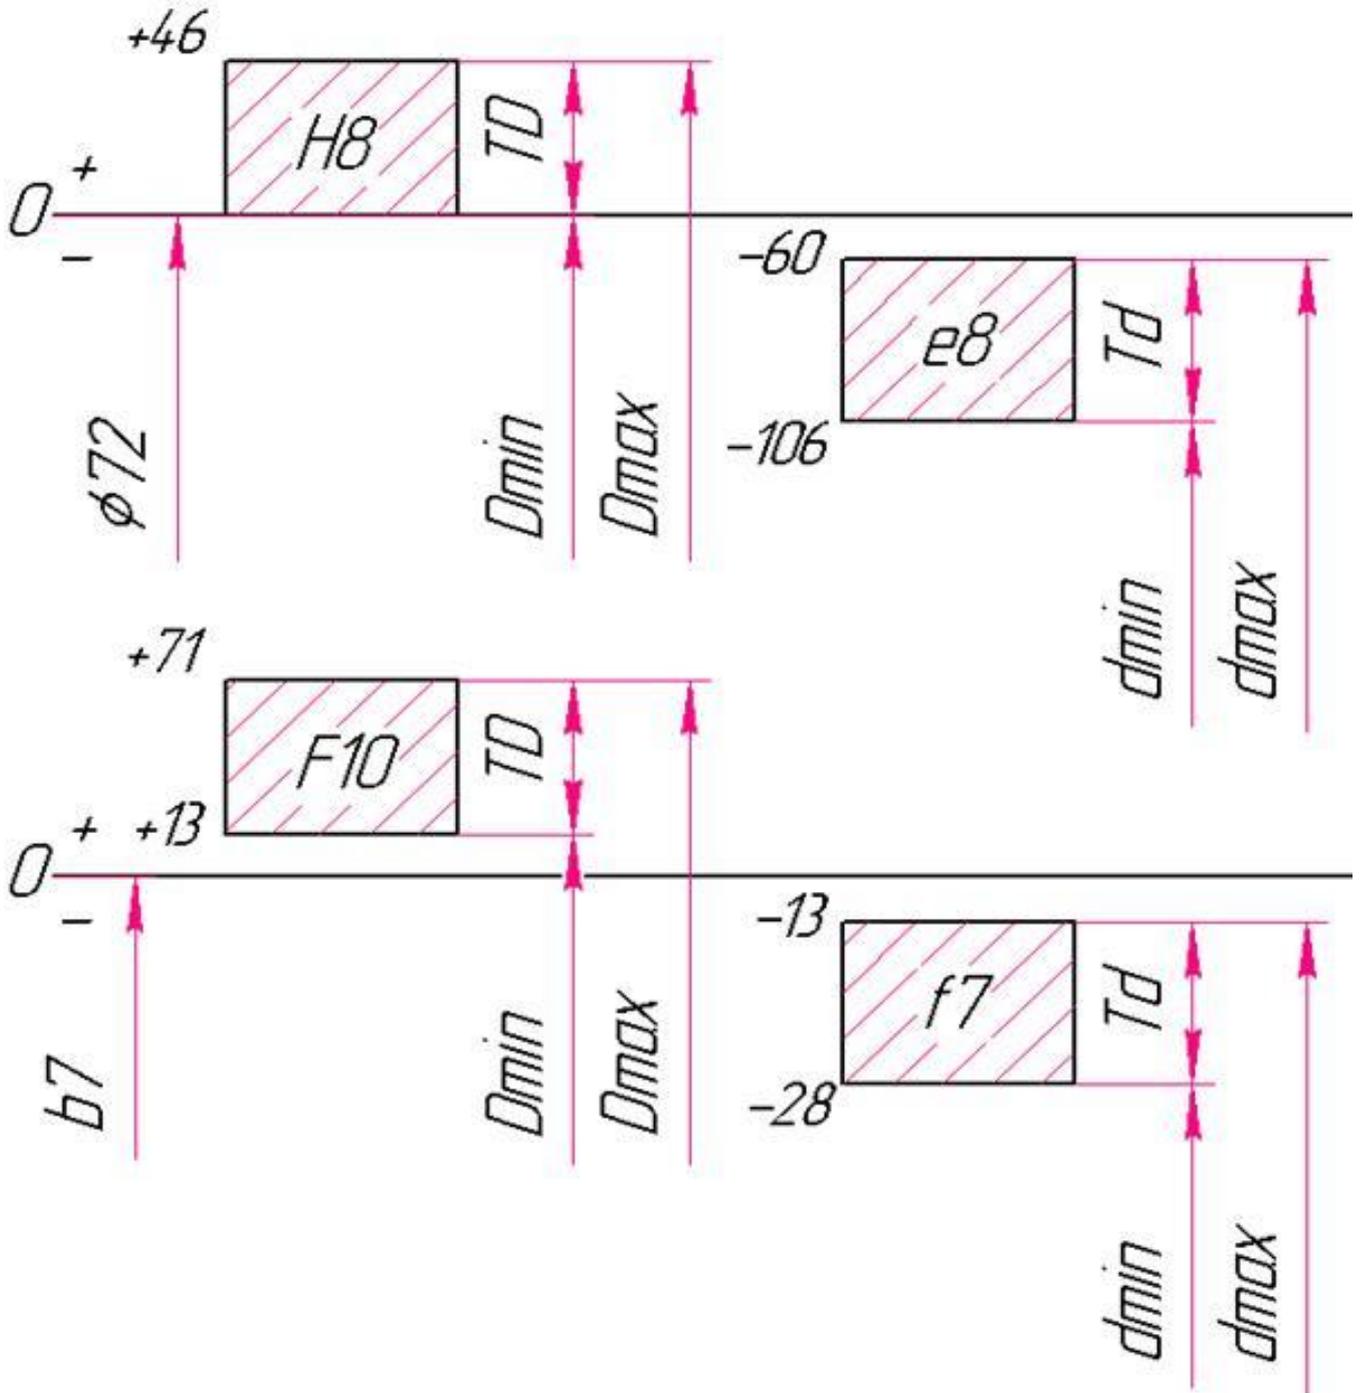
Схема полей допусков шлицевого соединения.
